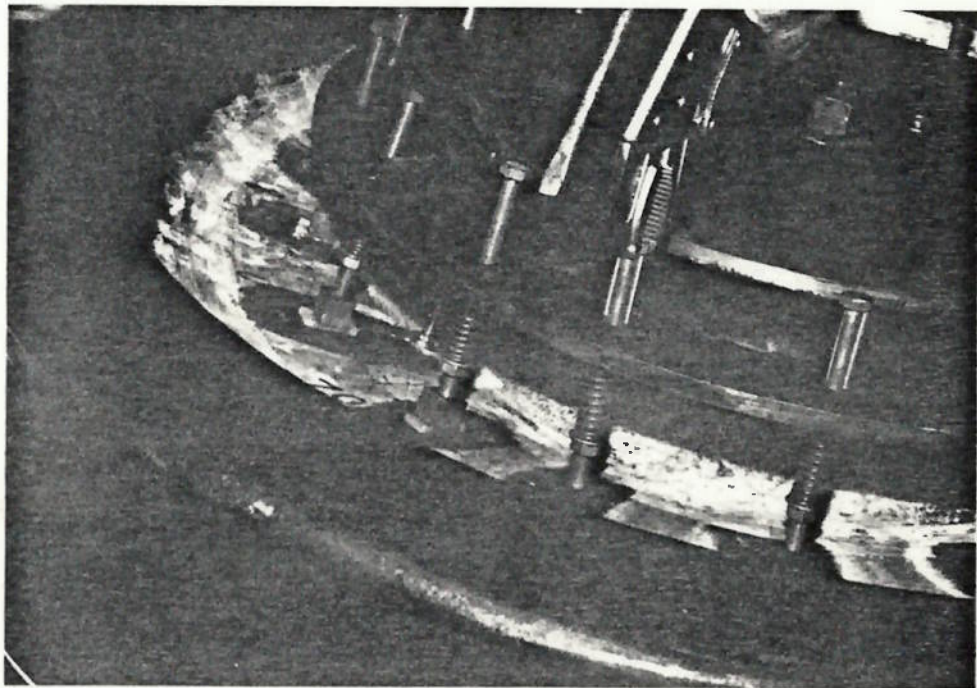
Detalhe do Posicionamento do Dispositivo de Fixação
